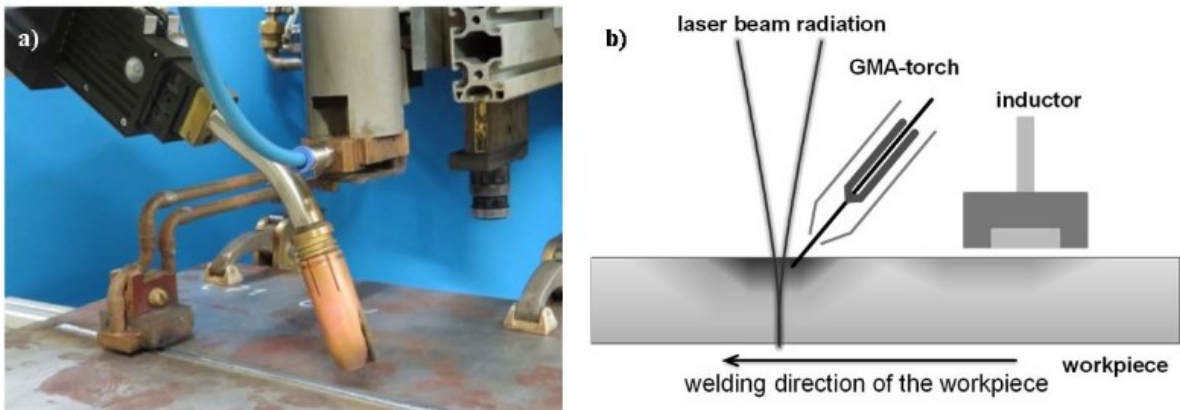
Setup, real(a) e esquemático(b) de indução associada ao processo de soldagem MAG/LASER
